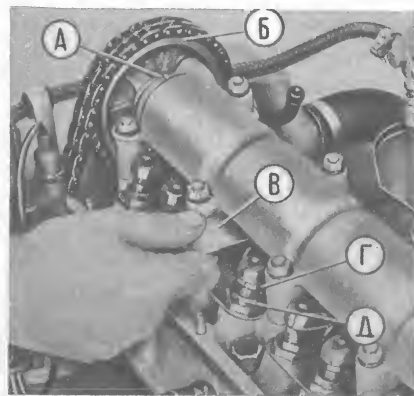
Регулировка распределительного механизма: А и Б — установочные метки распределительного вала; В — щуп толщиной 0,15 мм для проверки зазора; Г — шестигранник регулировочного болта; Д — контргайка.
